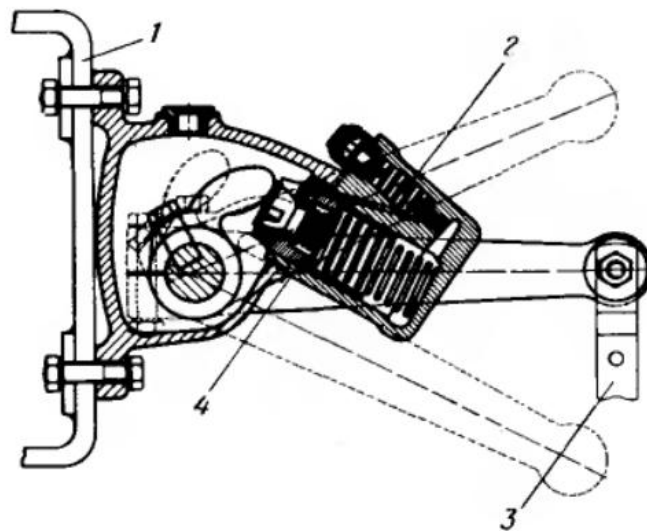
Односторонний рычажный амортизатор, демпфирующий только ход отбоя: 1– рама ТС; 2 – регулируемый клапан; 3 – крепление к подвеске; 4 – обратный клапан, возвратная пружина и рабочий поршень
